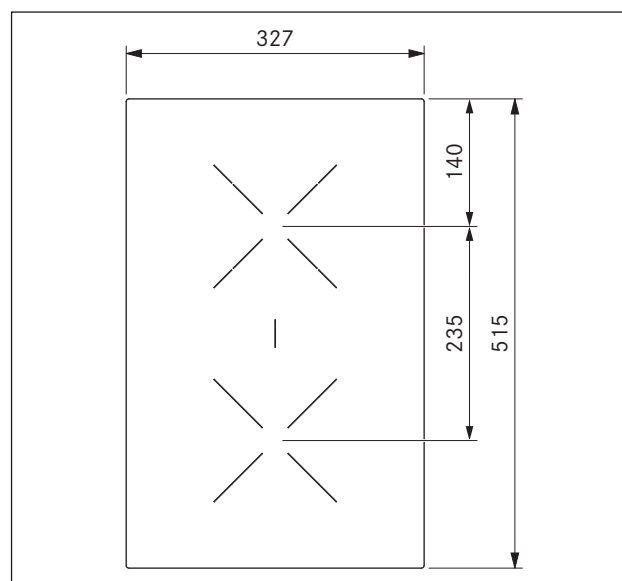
Dimensões do aparelho CKCB, vista de cima
